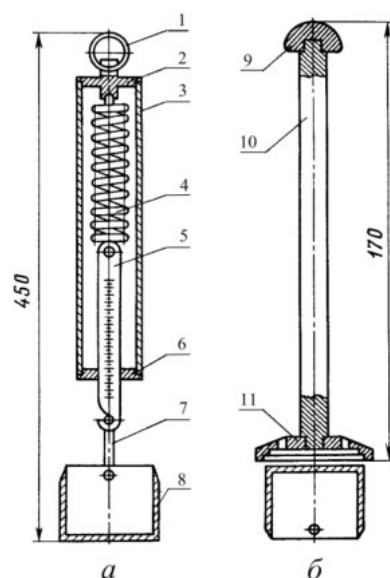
Пружинный плотномер: *а* – пружинные весы с мерным стаканчиком; *б* – пробоотборник; 1 – кольцо; 2 – втулка; 3 – корпус; 4 – пружина; 5 – шкала; 6 – направляющая шкала; 7 – дужка; 8 – мерный стаканчик; 9 – головка; 10 – корпус пробоотборника; 11 – опорная площадка
